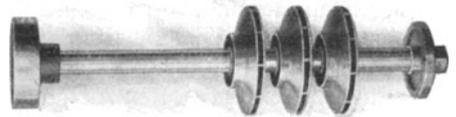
Rotor einer 3stufigen Turbinenpumpe.
